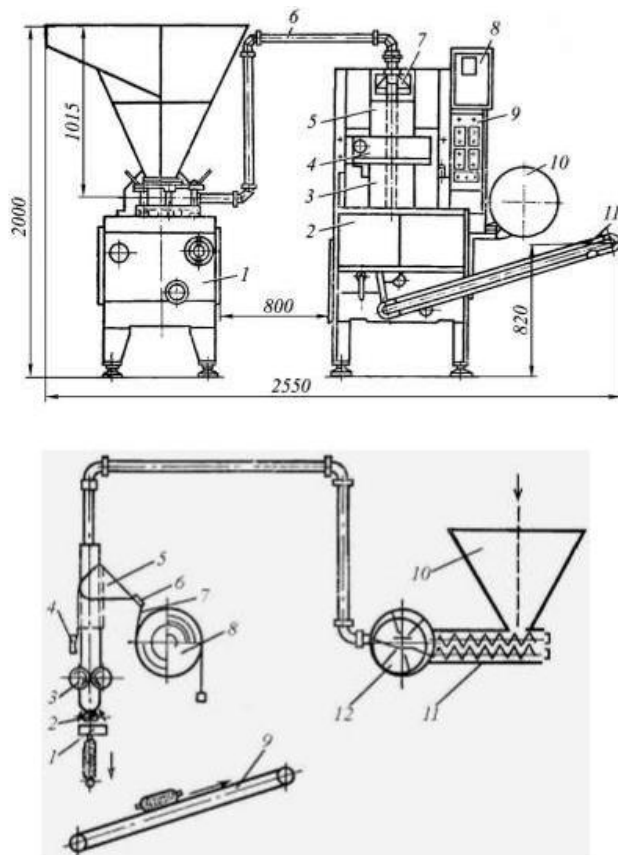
Агрегат М1-ФУР для формування ліверних ковбас:
